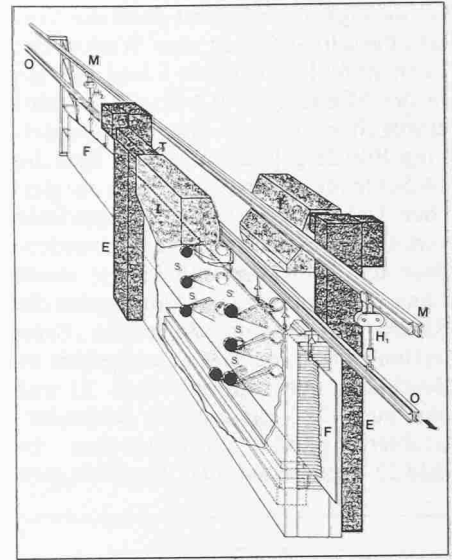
Perspektivische Skizze einer Peening-Anlage zur Behandlung langer, plattenförmiger Flugzeug-Flügel-Beplankungen zur Boeing 747 (Jumbojet) und 727 mit bis zu 31,6 m Länge und bis zu 3,6 m Breite. Maschine geliefert durch Wheelabrator Corp. Mishawaka USA und ausgerüstet mit 14 Schleuderrädern.
